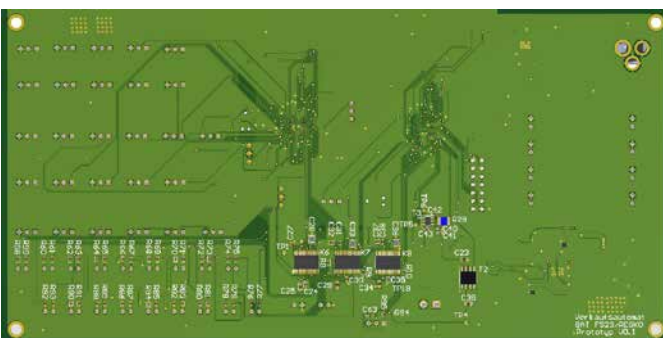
Steuerplatine in der Bottom-View Ansicht.
